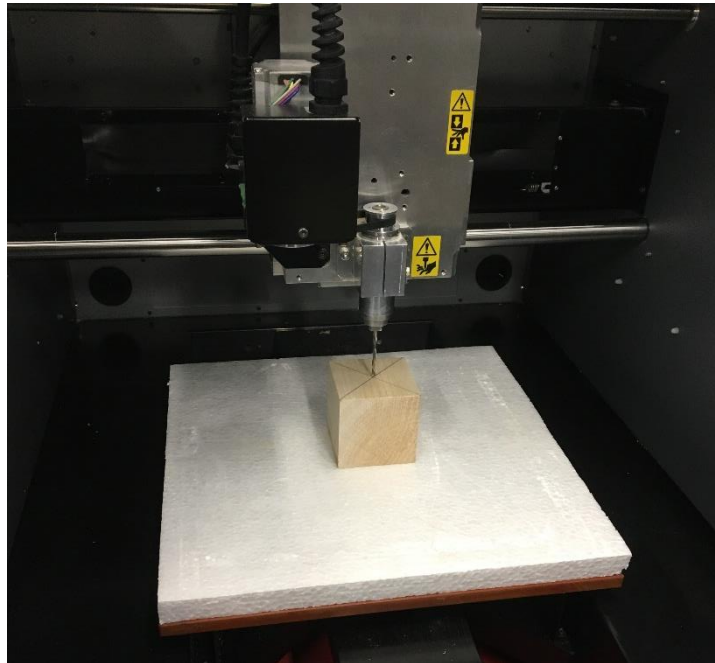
Maquinado Fresadora CNC – Centrado manual de herramienta
